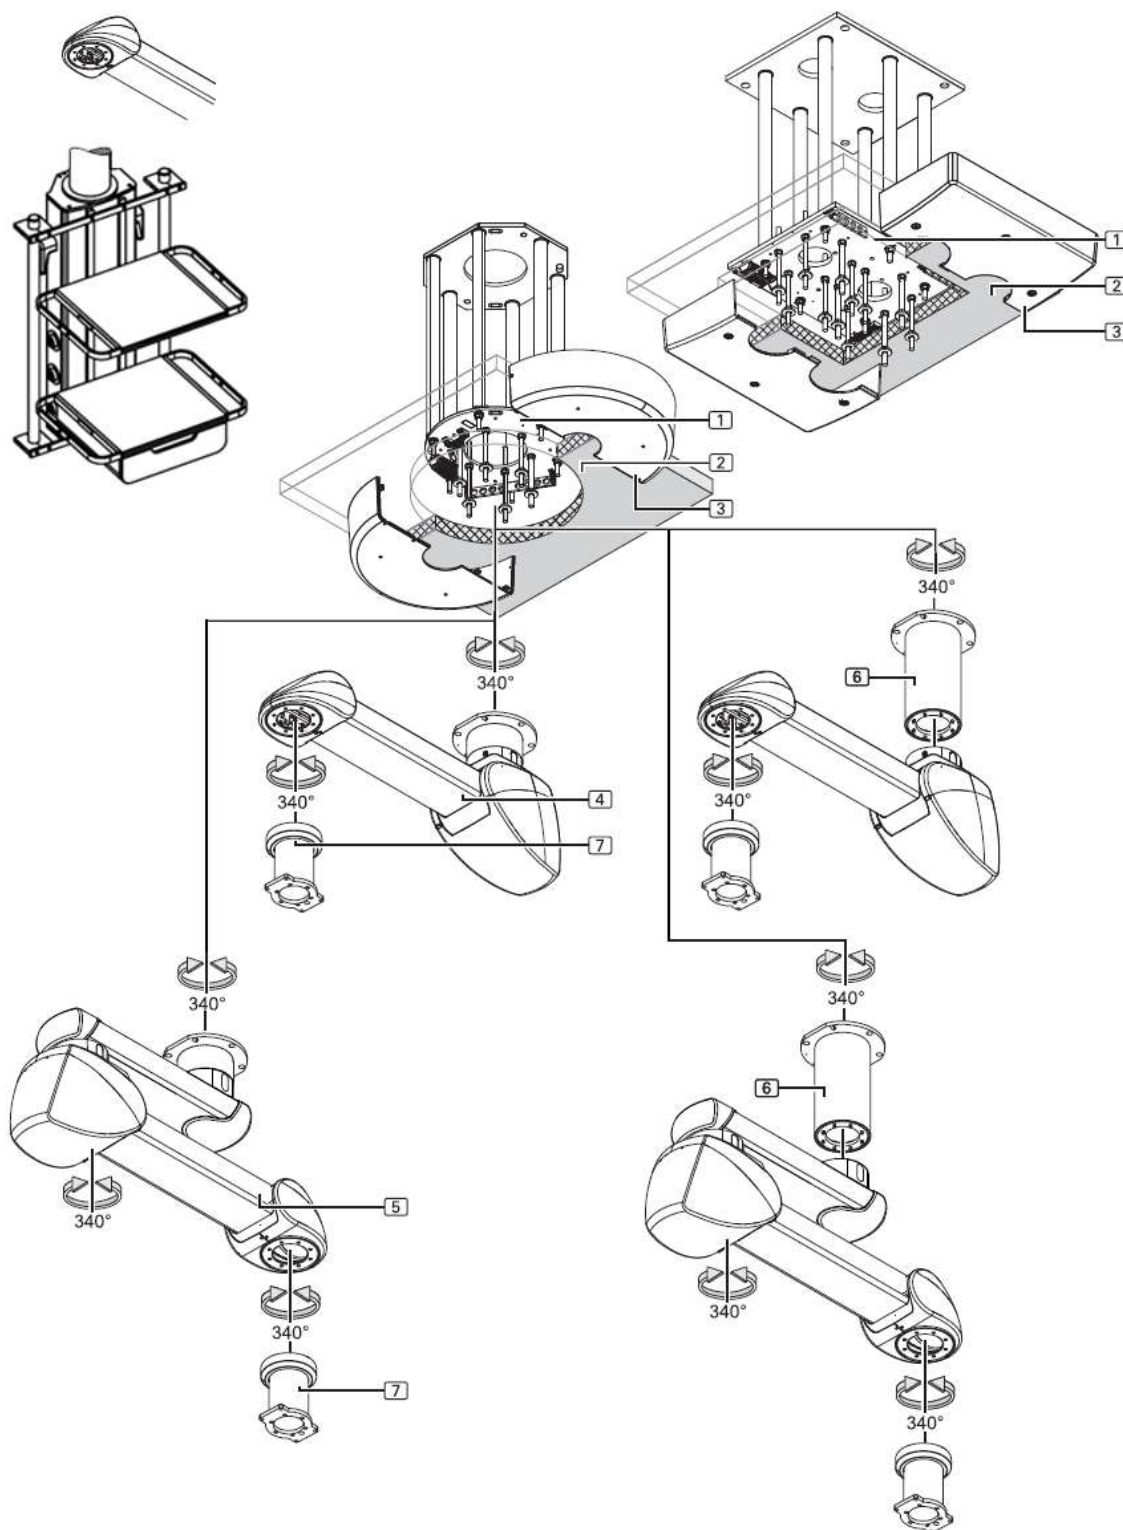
COLUMN FRICTION, COLUMN AIR, COLUMN E-BRAKE
